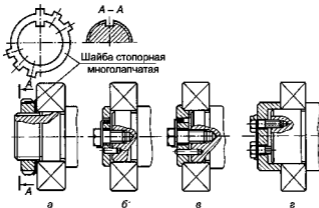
Крепление подшипников на валах: а – круговой шлицевой гайкой; б, в, г – концевой шайбой
